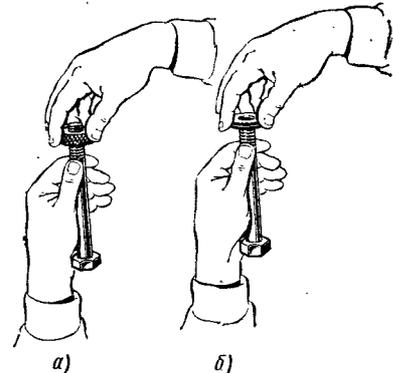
Проверка резьбы резьбовыми калибрами-кольцами
